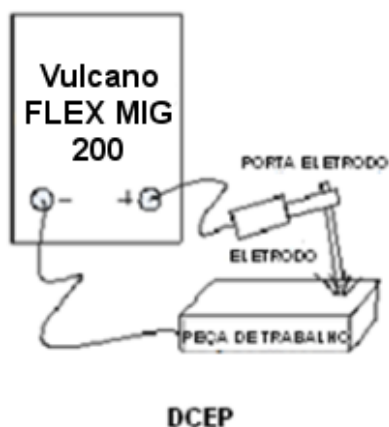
Conexão positiva para soldagem com eletrodo revestido
